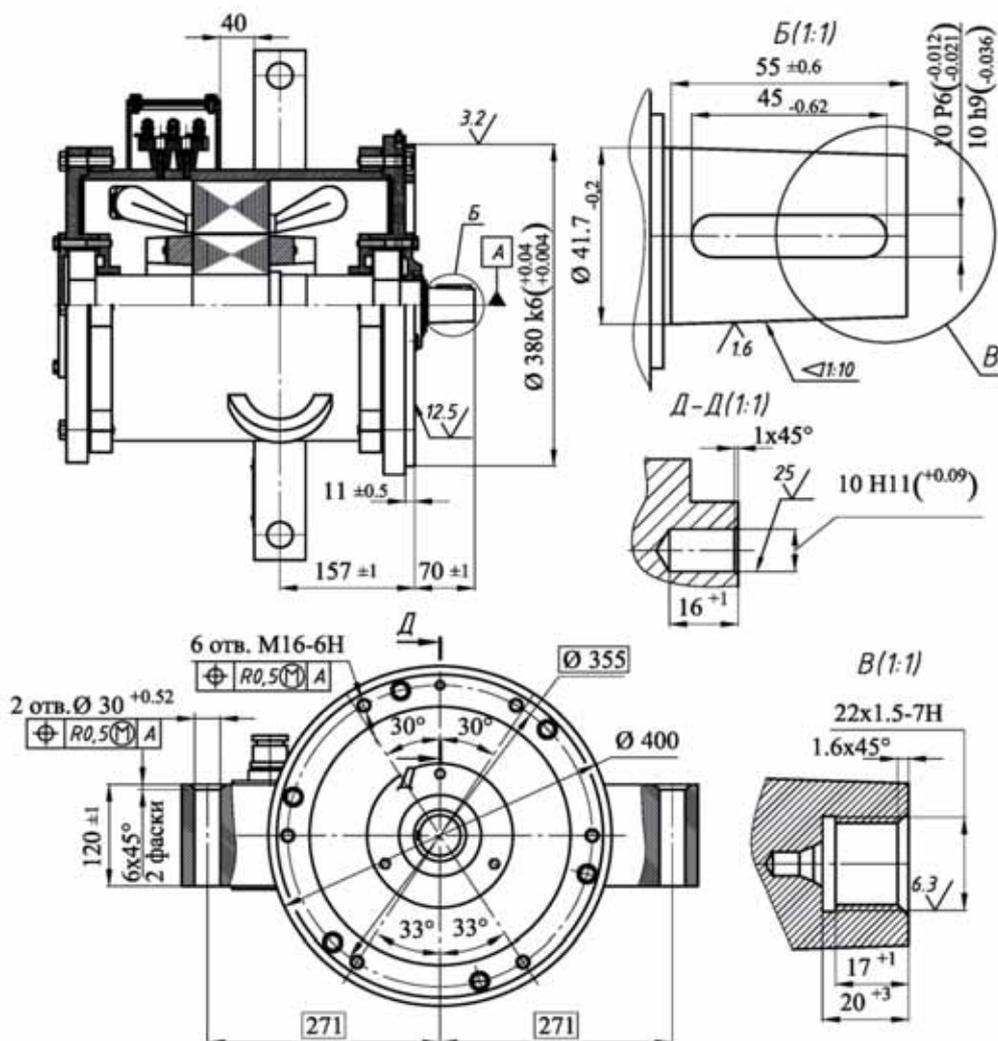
Габаритные и установочно-присоединительные размеры МАКУ160М6
